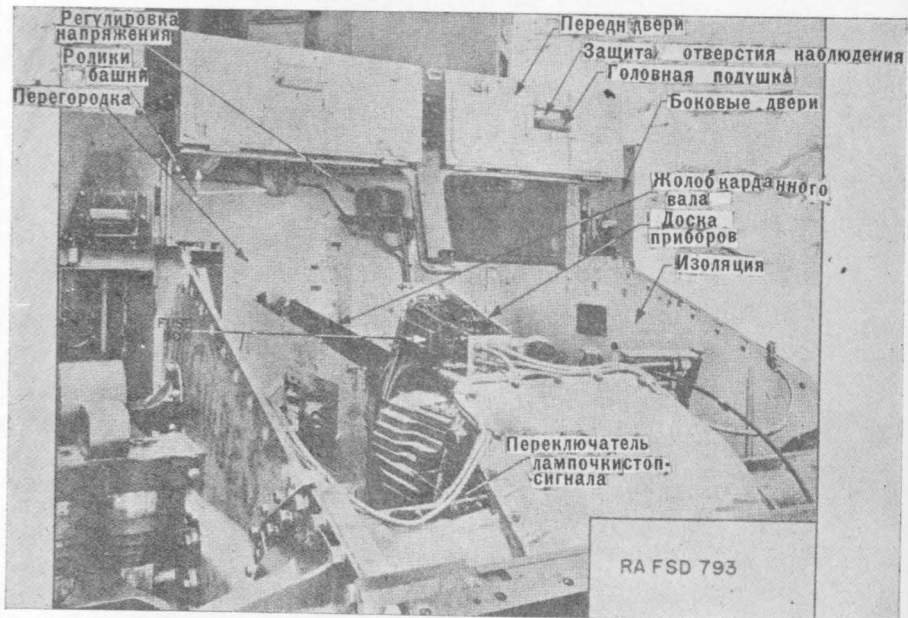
Корпус танка. Внутренний вид боевого отделения.
